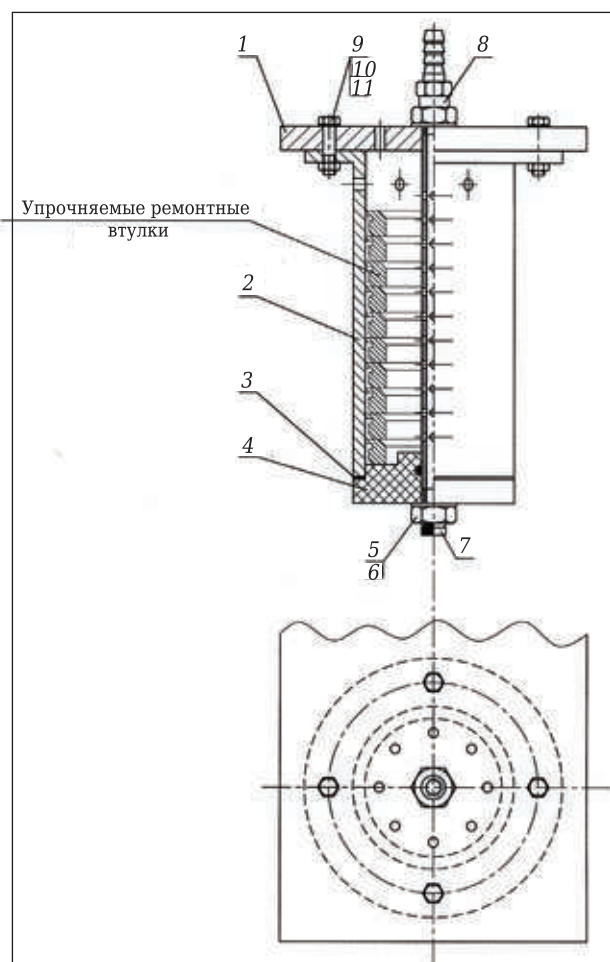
Общий вид приспособления, используемого для закрепления и оксидирования втулок: 1 — фторопластовая пластина; 2 — цилиндрический электрод-1; 3 — прокладка; 4 — крышка; 5 — гайка; 6 — шайба; 7 — электрод-2 с пробкой; 8 — штуцер; 9 — болт; 10 — шайба; 11 — гайка
